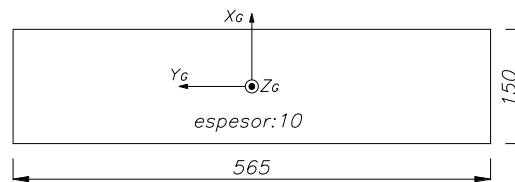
21. Modelo preliminar plancha de apoyo del pie.
